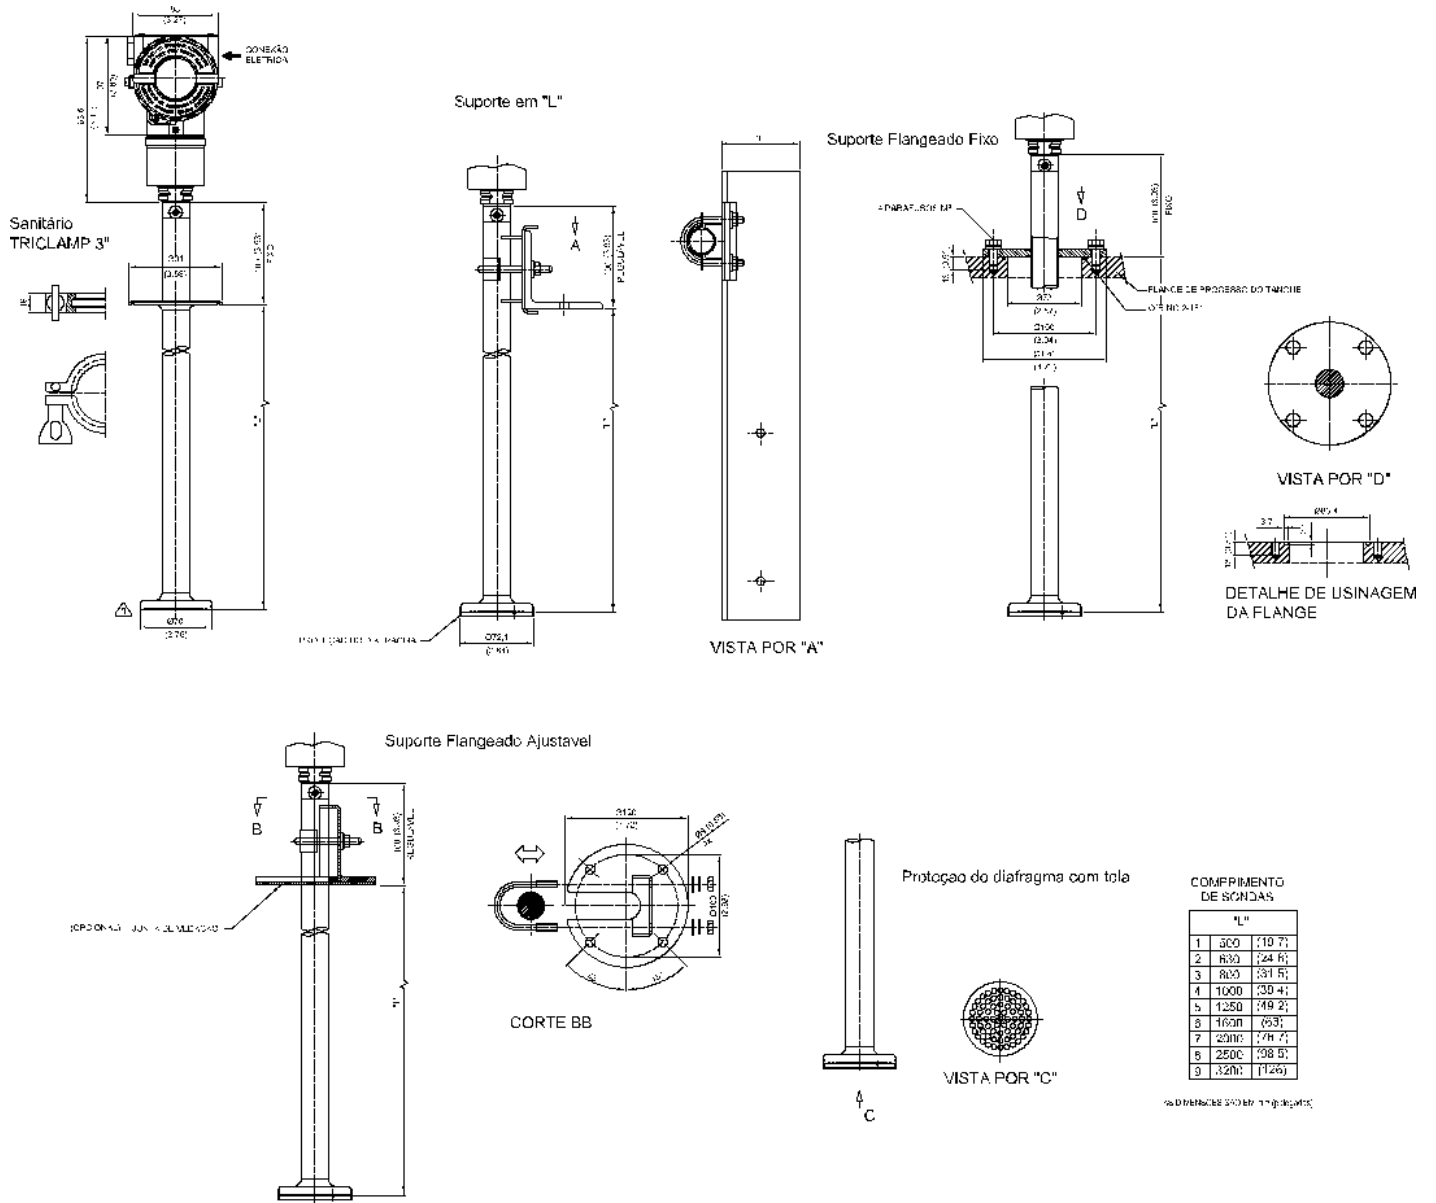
(d)- Desenho Dimensional de Montagem do LD292 – Nível (Inserção)
